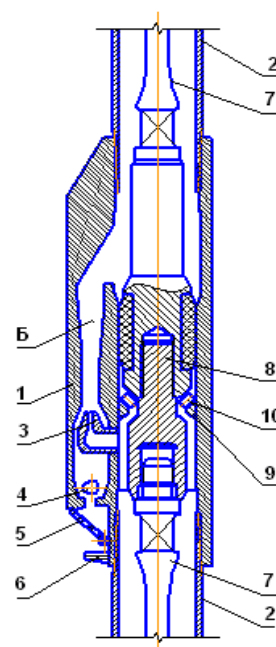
Автоматическое устройство для перепуска затрубного газа
